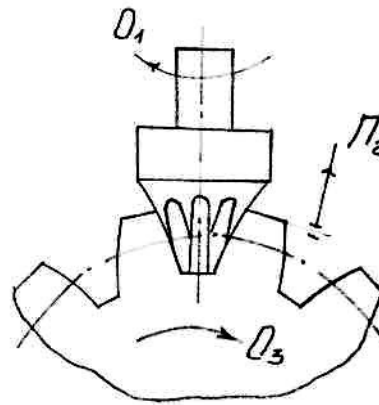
Схема обробки пальчиковою фрезою.
